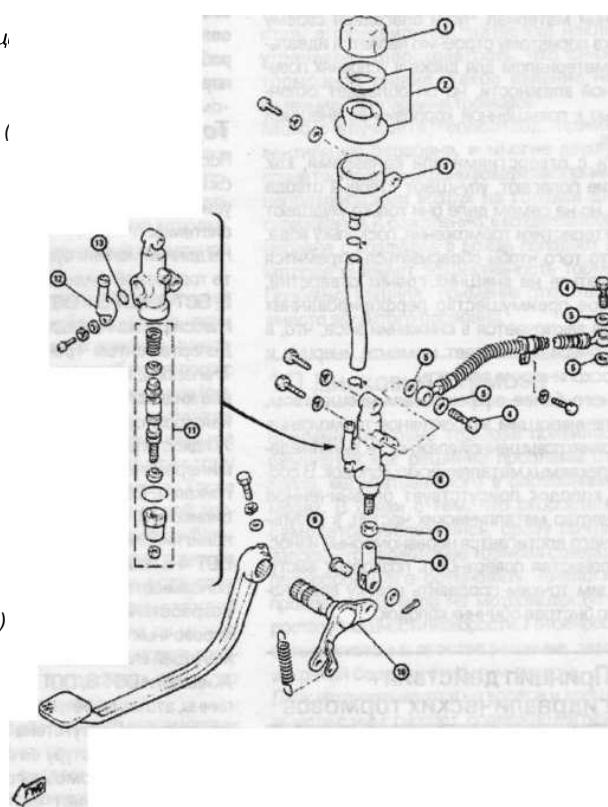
Детали типичного главного цилиндра заднего тормоза
